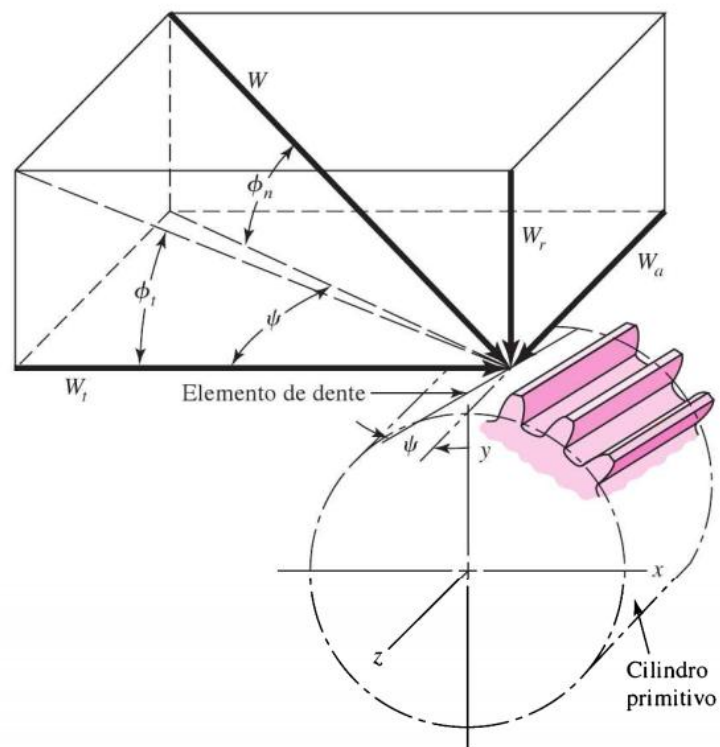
Forças agindo sobre dentes de uma engrenagem helicoidal.
